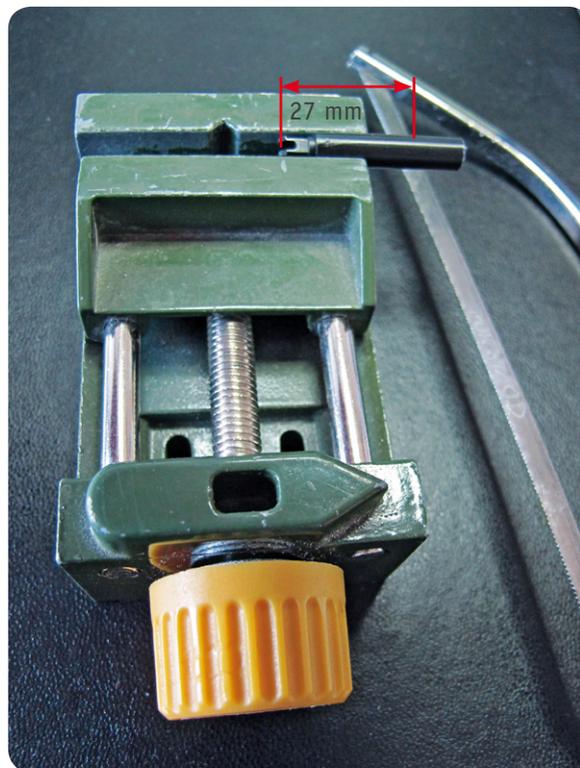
Die Potentiometerachsen sind auf 27 mm Länge zu kürzen.
